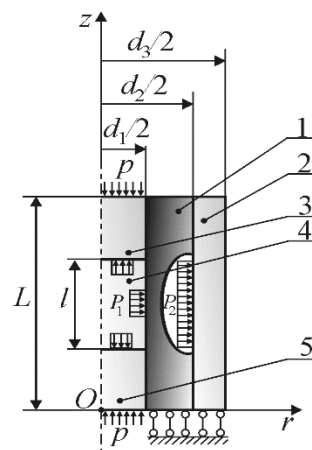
Розрахункова схема прес-форми для виготовлення суцільних виробів з порошків: 1 – центральний стержень; 2 – вкладиш; 3 – матриця; 4, 6 – пуансони; 5 – брикет з порошку
